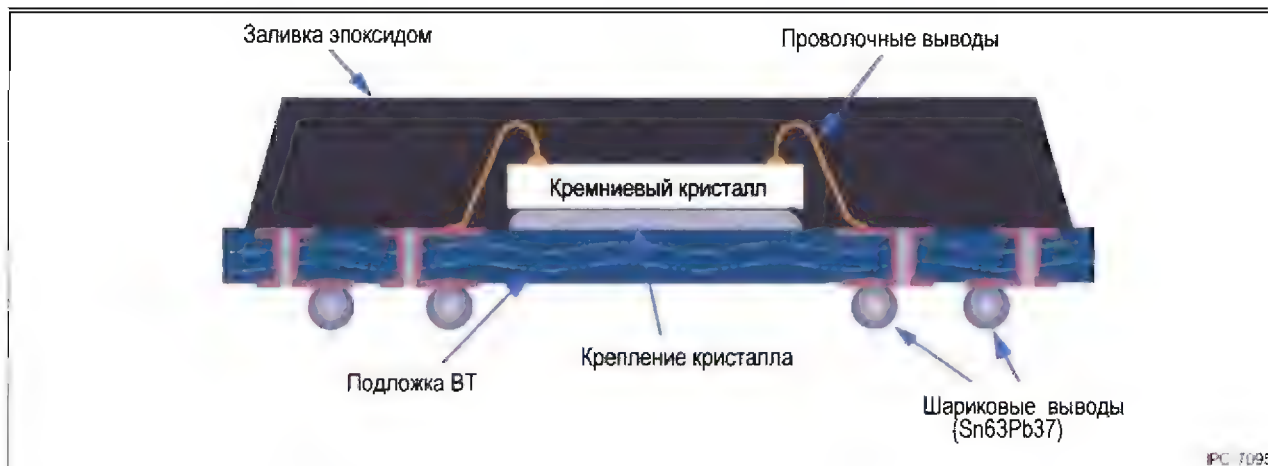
Пластиковый корпус BGA, кристалл с разваркой проволочных соединений
